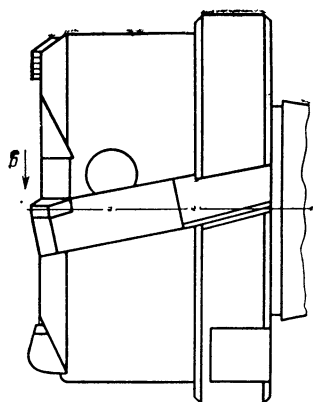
Геометрические параметры режущей части торцевой фрезы.
